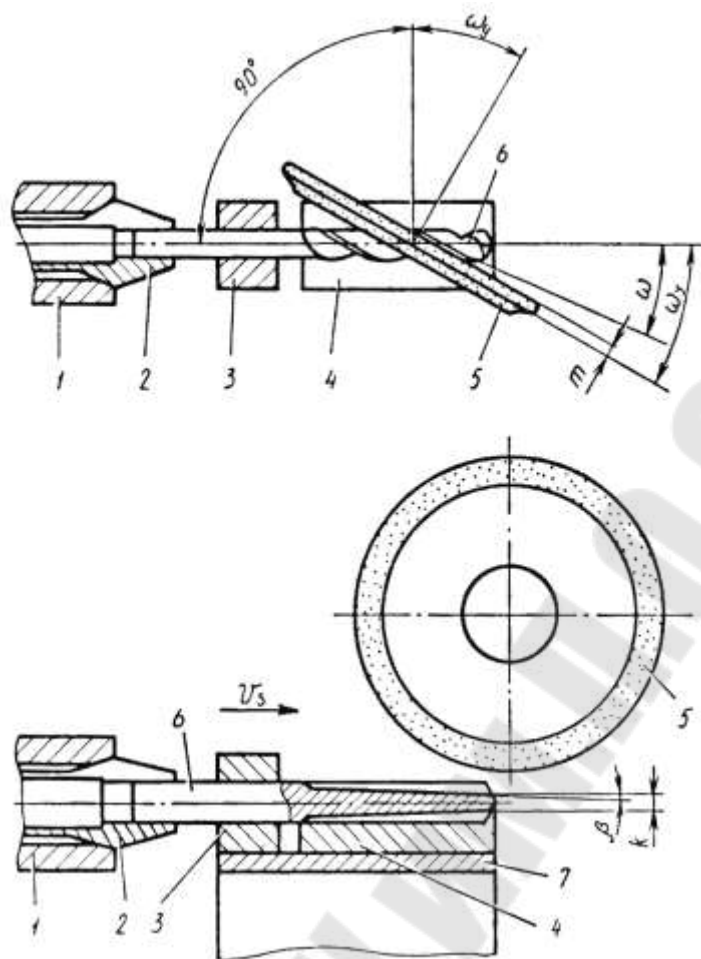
Расположение заготовки и абразивного инструмента при вышлифовке канавок инструмента: 1 – цанговая оправка; 2 – цанга; 3 – очко; 4 – люнет; 5 – абразивный инструмент; 6 – обрабатываемый инструмент; 7 – регулировочная прокладка;  $\omega$  – угол наклона канавок;  $\omega_y$  – угол установки абразивного инструмента;  $k$ ,  $\beta$  – диаметр и угол подъема сердцевины
